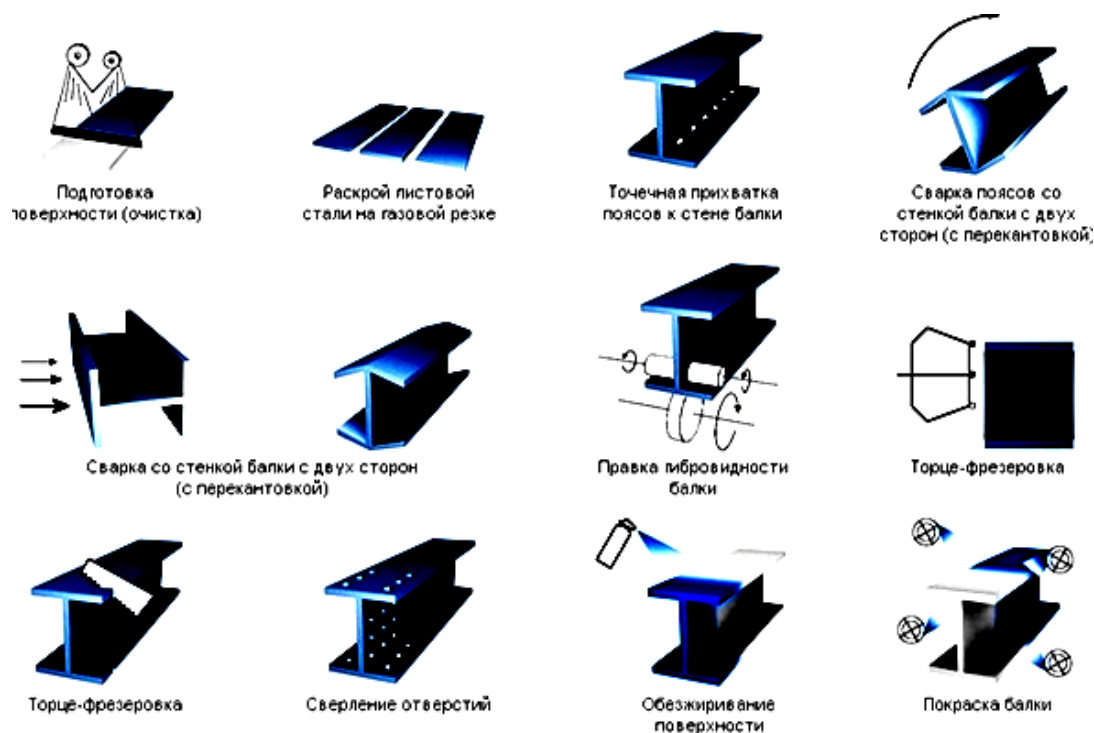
Этапы изготовления сварной двутавровой балки
